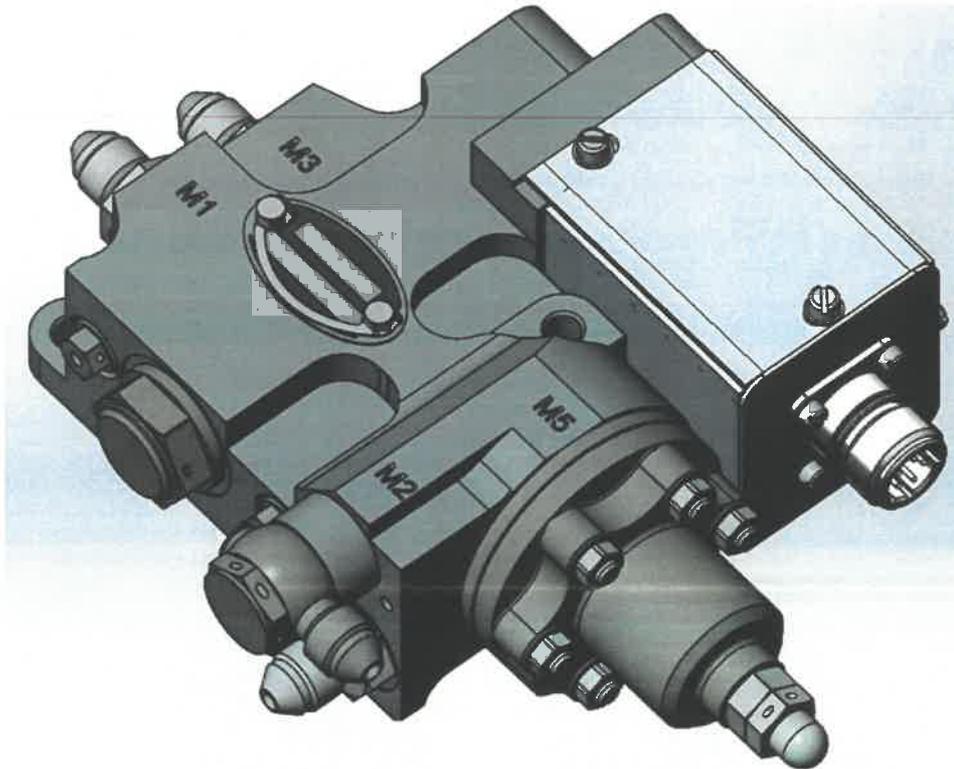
Общий вид агрегата АЗ-157ВР01.
